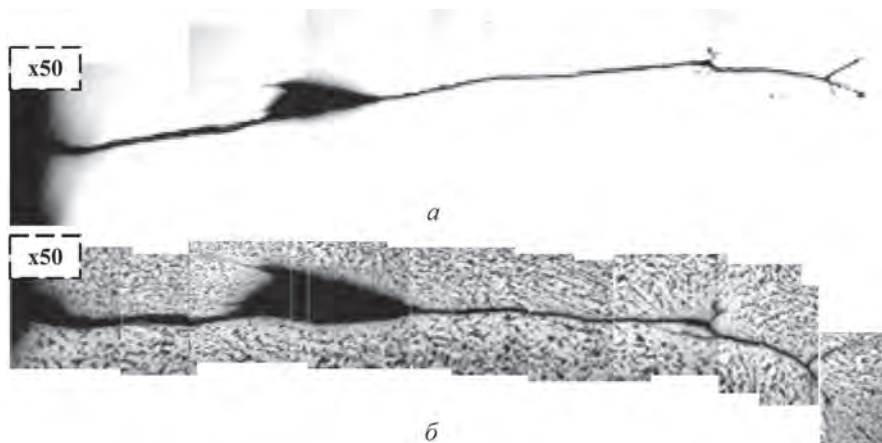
Трещины в поперечном сечении микрошлифа горячекатаной заготовки: *a* – нетравленный образец; *б* – травленный в 4%-ном спиртовом растворе азотной кислоты
